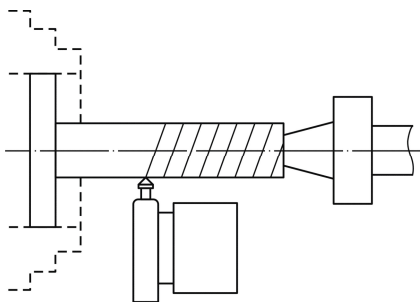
Схема нанесения регулярного микрорельефа на поверхность плунжера ТНВД на токарном станке
